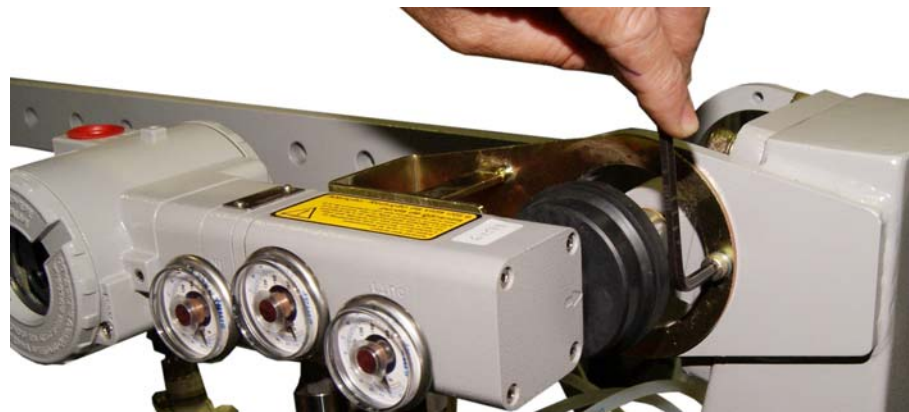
Suporte do Posicionador - ACP Rotativo
